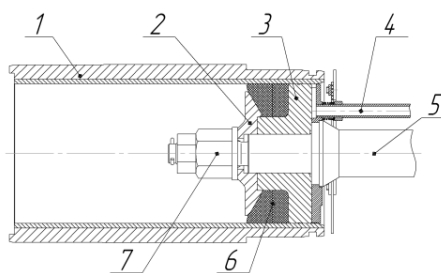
Цилиндровая группа: 1 – втулка цилиндровая; 2 – шайба; 3 – сердечник; 4 – подвод СОЖ; 5 – шток поршня; 6 – манжета поршня; 7 – гайка крепления поршня
